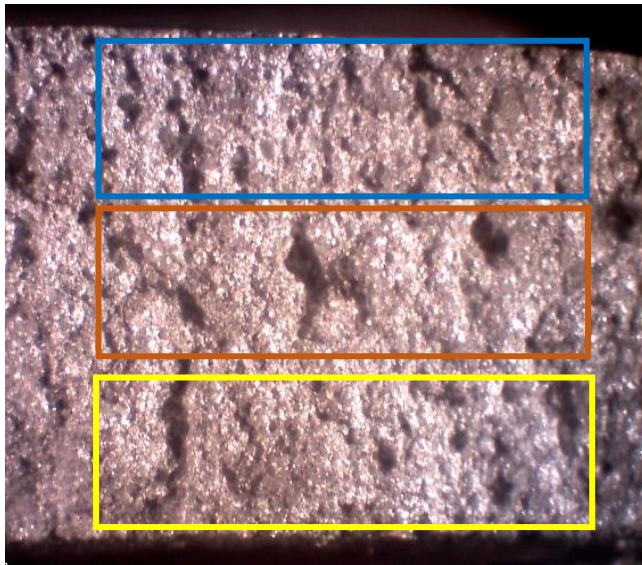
Fractura de la sección 1 de la probeta sin defecto utilizada en el ensayo de tracción.
